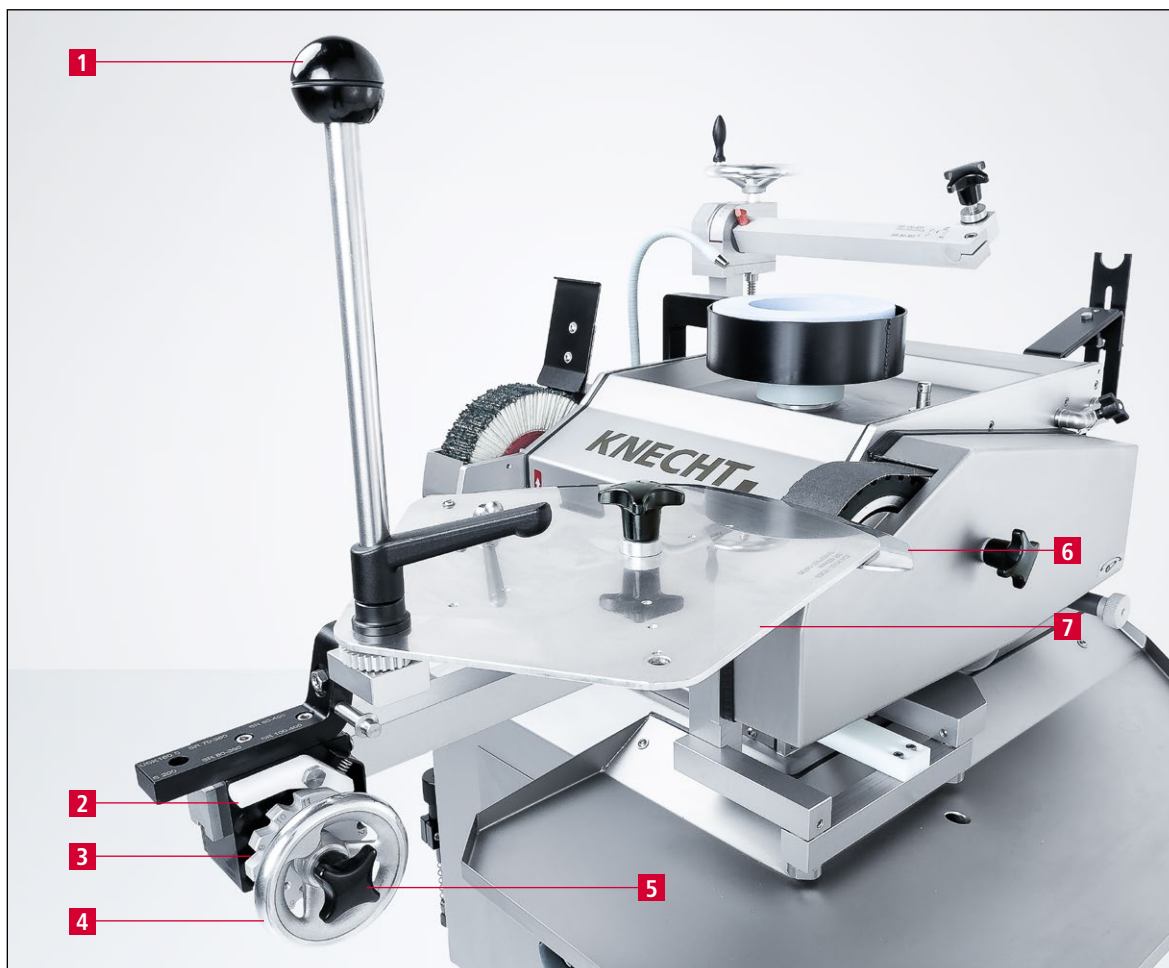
Общий вид устройства для ленточной заточки HV 261
